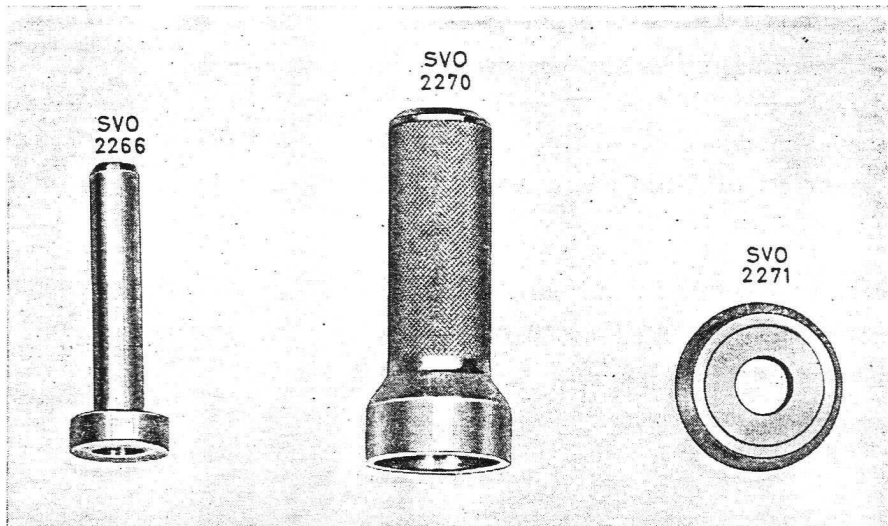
Spezialwerkzeuge für Wasserpumpe
